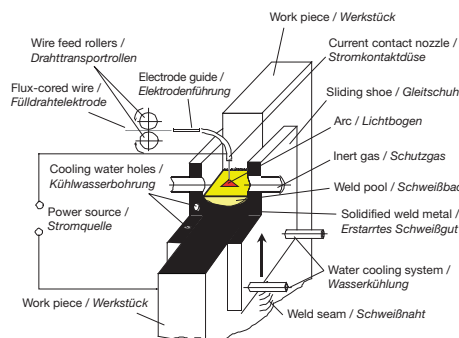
Verfahrensprinzip des Elektrogasschweißens
